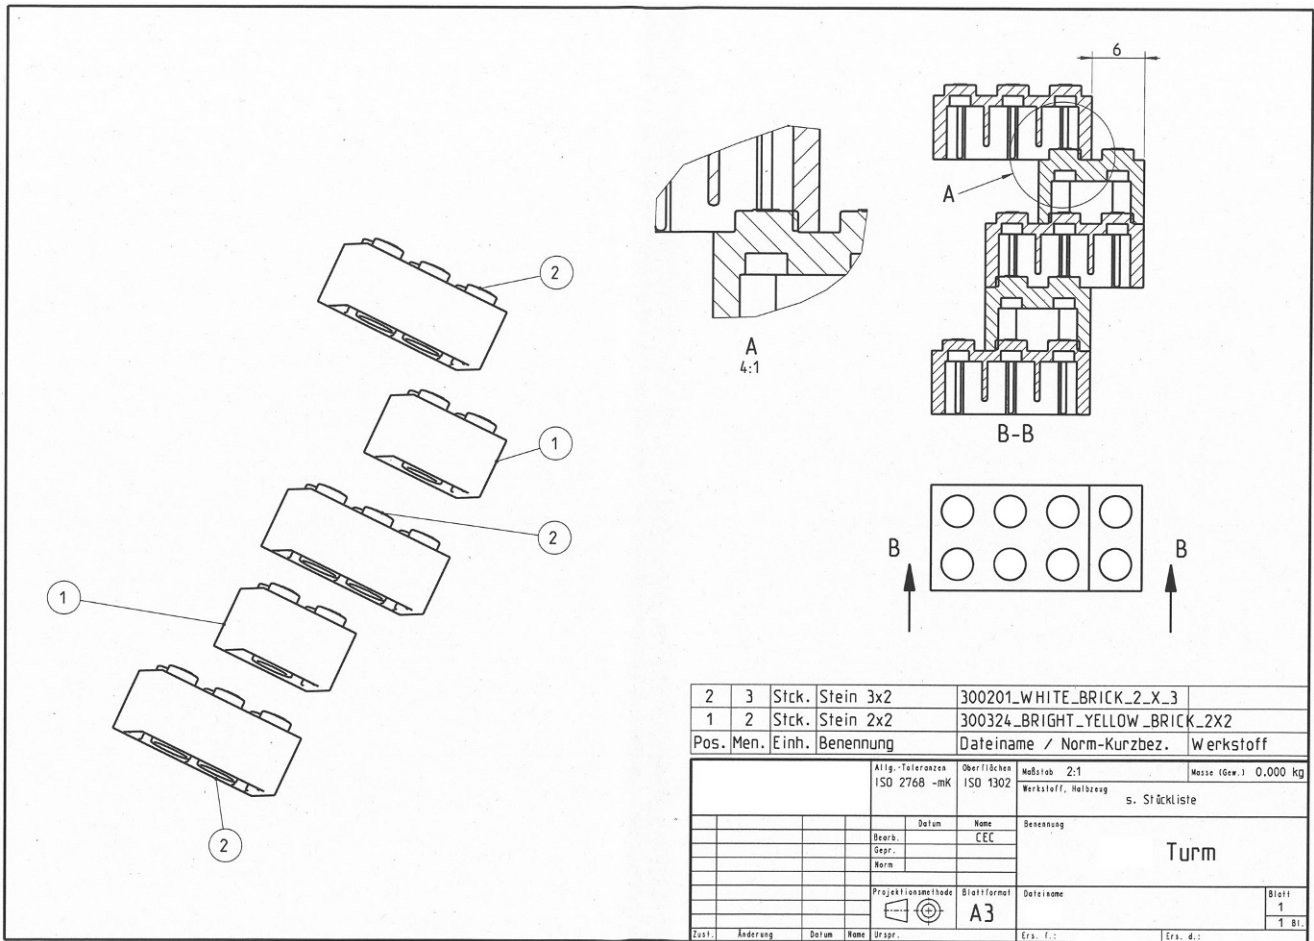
Explosionszeichnung des Klemmbaustein-Turms
